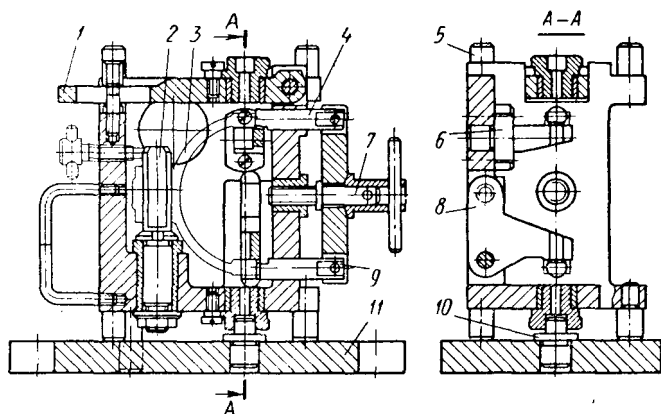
Кантующееся приспособление для обработки отверстий в вилках
